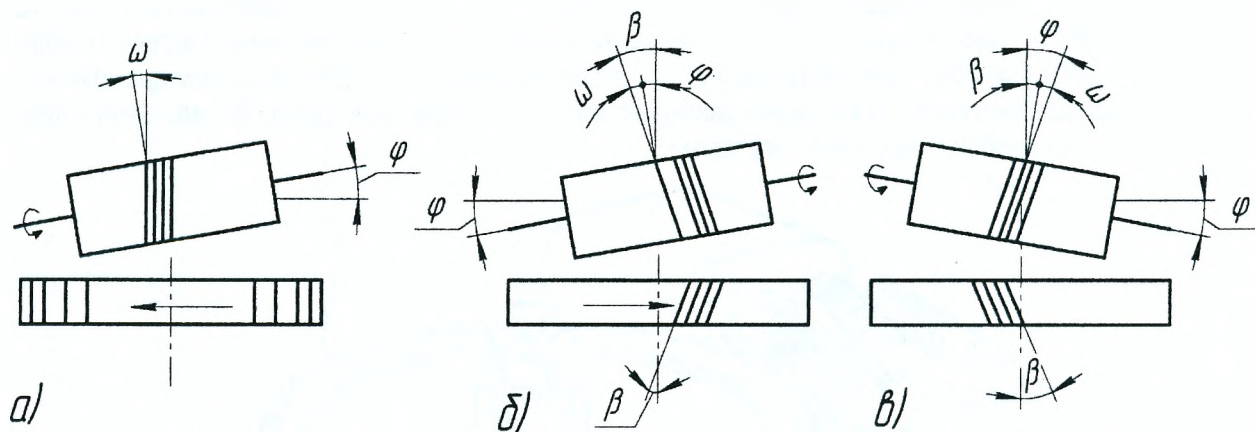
Схема образования зубьев цилиндрического косозубого колеса
